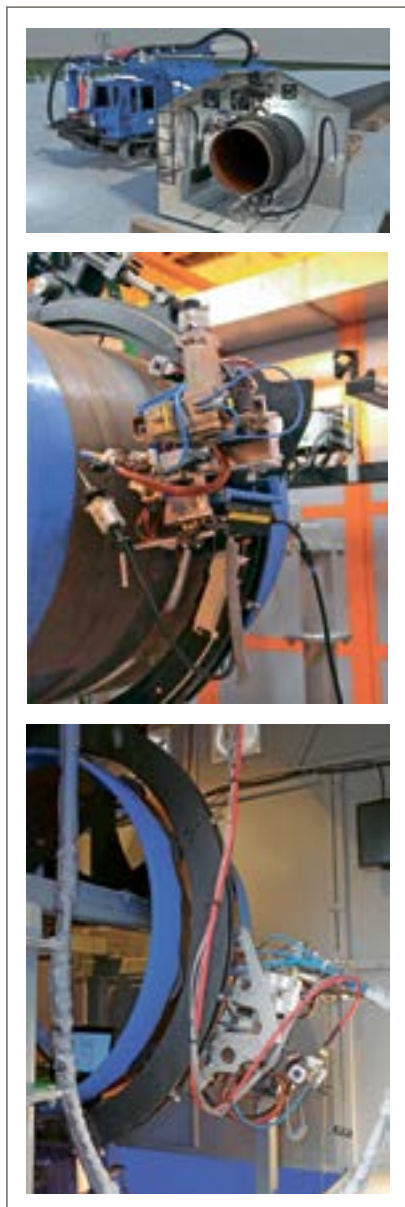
Навесное сварочное оборудование (орбитальный манипулятор) установки УЛСТ
